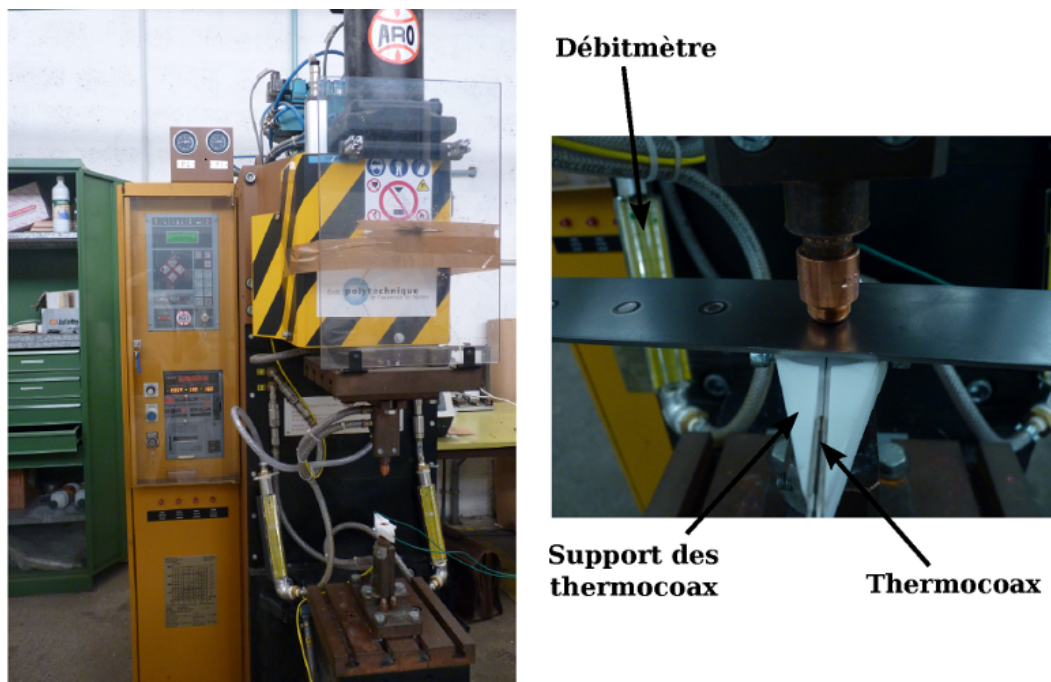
Vue d'ensemble de la soudeuse ARO type 1000.
